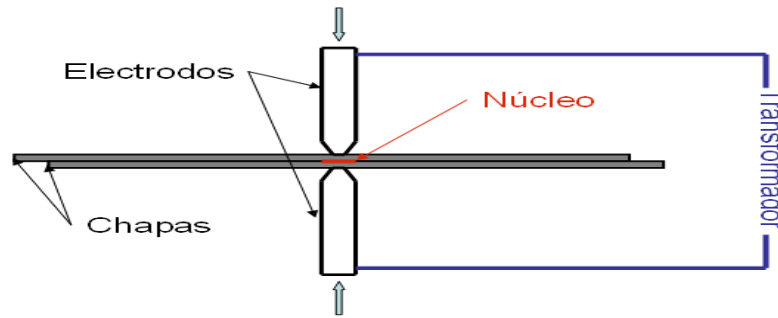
Diagrama de una máquina soldadora por puntos
